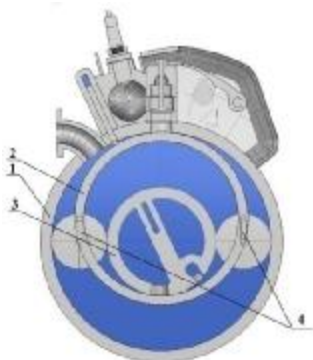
Конструктивная схема двигателя: 1- наружный корпус; 2- кольцевой поршень; 3- внутренний корпус; 4- кривошипы
